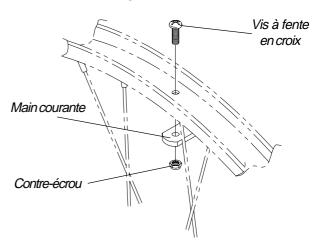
REMPLACEMENT DE LA MAIN-COURANTE
